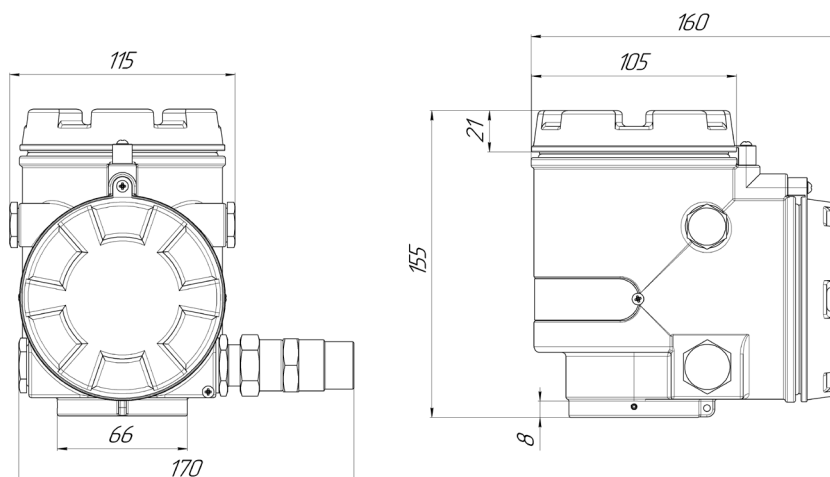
Габаритные размеры двухкамерного корпуса
